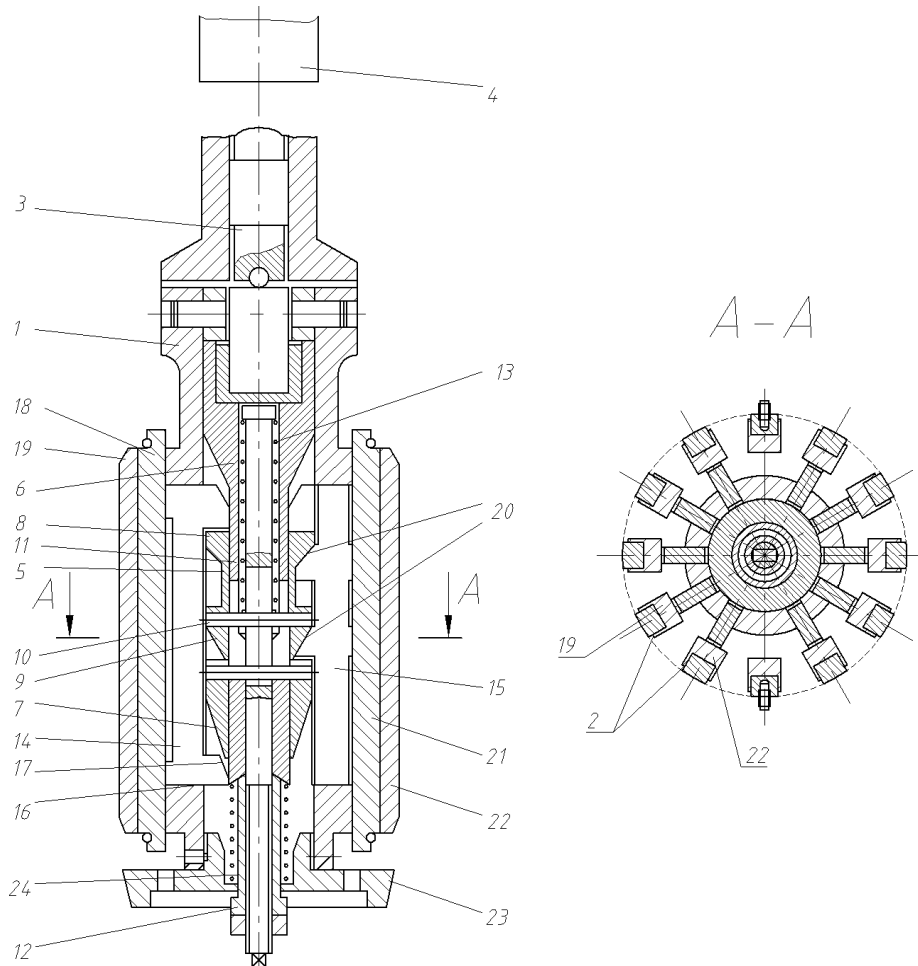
Схема головки для рівно-вершинного хонінгування циліндрів: 1 – корпус; 2 – пази; 3 – шток; 4 – гідропривід; 5 – вісь; 6 і 7 – конічні втулки; 8 і 9 – здвоєні конуси; 10 – зчіпка; 11 – тяга; 12 – упор; 13 – пружина; 14 і 15 – штовхані; 16 і 17 – контактні площадки; 18 – колодка; 19 – грубозернисті бруски; 20 – робочі площадки; 21 – колодки; 22 – дрібнозернисті бруски; 23 – уловлювач; 24 – виштовхуюча пружина.
